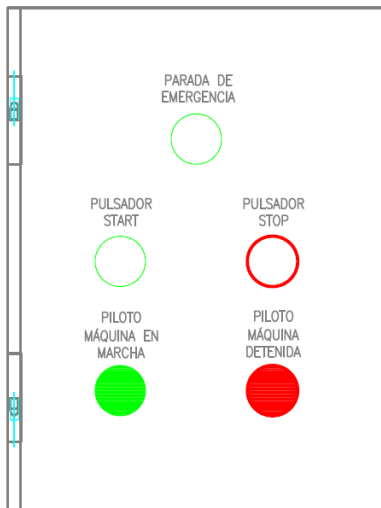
Detalles constructivos tablero de mandos (parte exterior).
